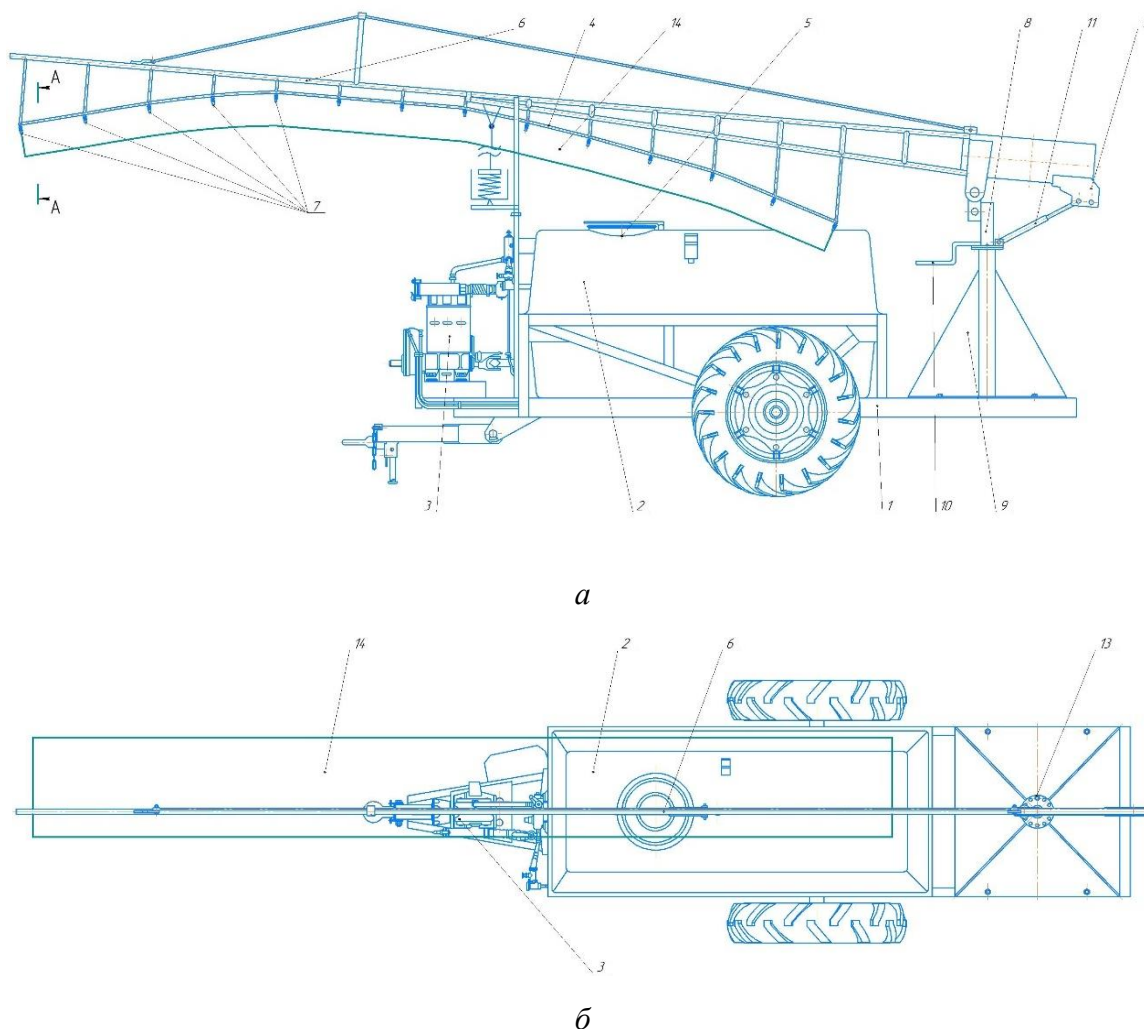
Опрыскиватель: *а* – вид слева; *б* – вид сверху; 1 – рама; 2 – емкость; 3 – насос; 4 – коммуникации; 5 – очистка; 6 – штанга; 7 – распылители; 8 – стойка; 9 – опора; 10 – рукоятка; 11 – гидроцилиндр; 12 – фланец; 13 – палец; 14 – защитно-камерное устройство
